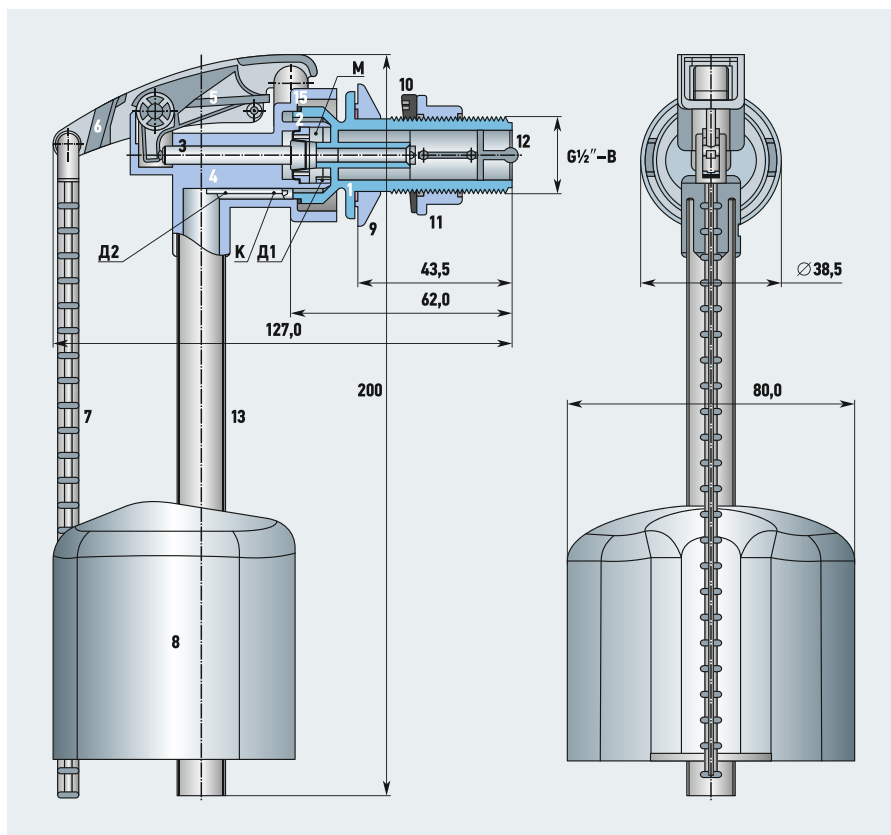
Конструкция новой наполнительной арматуры противодействия боковой подводки (1 — штуцер; 2 — манжета чулочного типа; 3 — шток; 4 — корпус; 5 — вспомогательный рычаг; 6 — основной рычаг; 7 — тяга; 8 — поплавок; 9 — эластичная конусная прокладка; 10 — косая шайба; 11 — гайка; 12 — фильтр грубой очистки; 13 — противошумная трубка, которая также служит и как направляющая поплавка 8)
